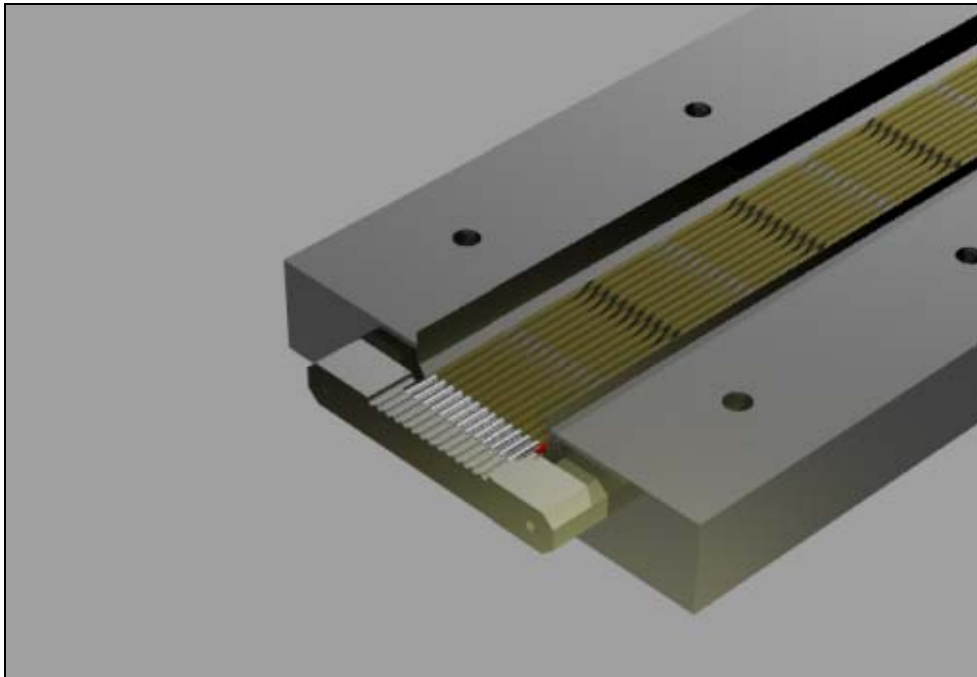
Pressore metallico durante la fase conclusiva di assemblaggio dell'interfaccia.
